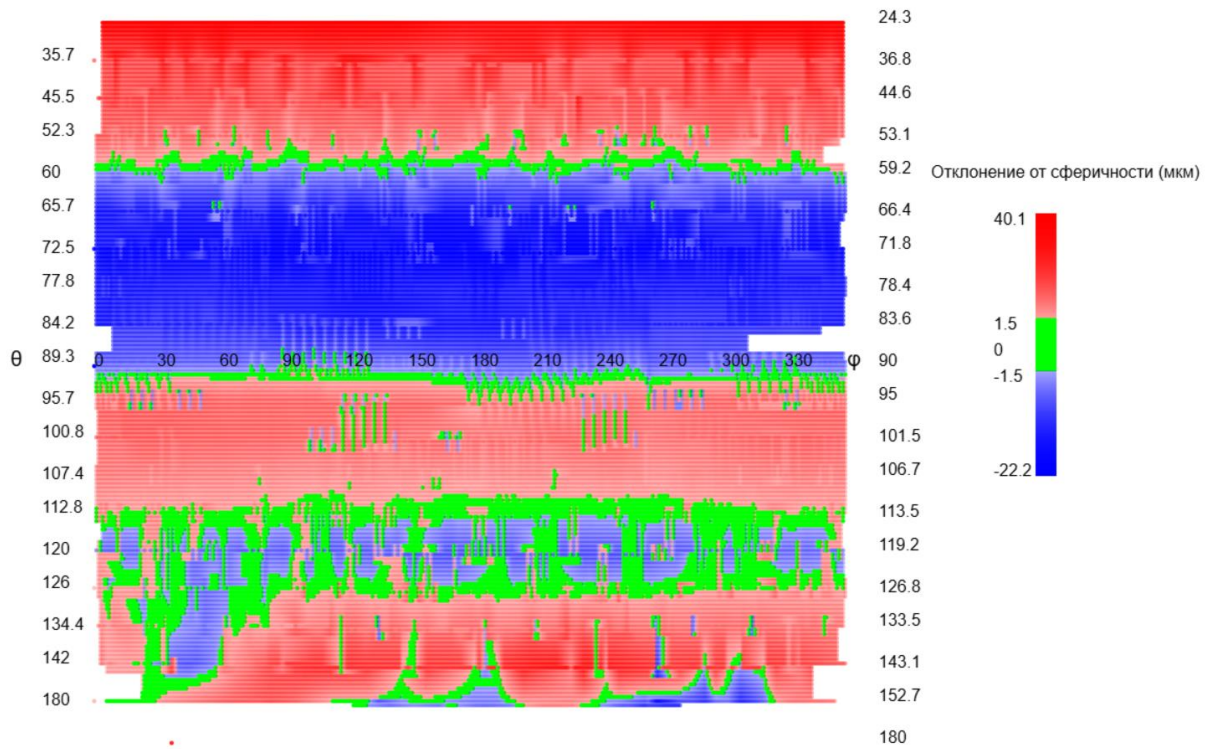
Развертка сферической поверхности шарового пальца №2 до притирки
